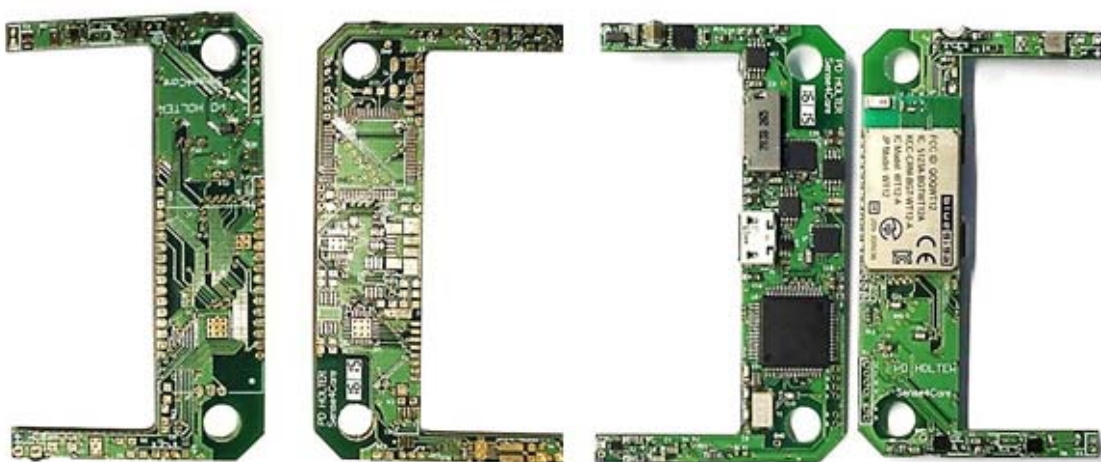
Fotografías de la PCB del PD-logger, a la izquierda sin componentes soldados y a la derecha completamente finalizada.
